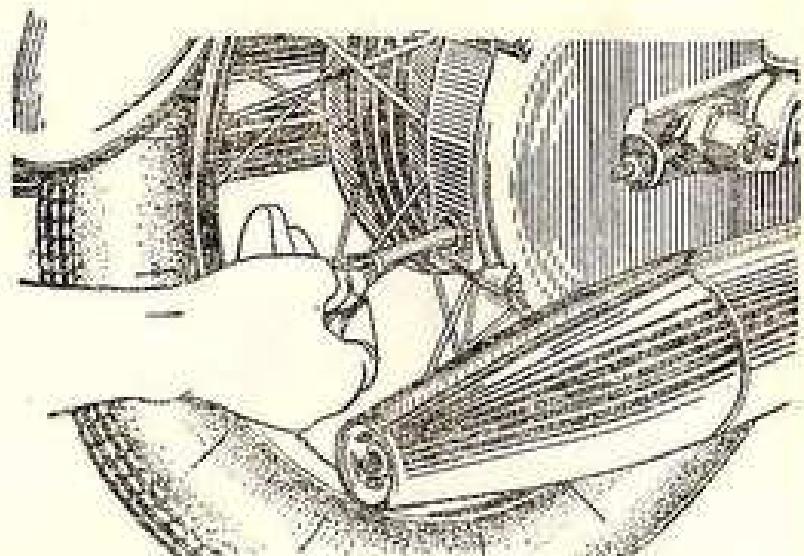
РЕГУЛИРОВКА НОЖНОГО ТОРМОЗА
